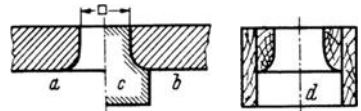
Abrundungen in Kernkästen. a = Werkzeichnung; b = Werkaufriß; c = Kern; d = Kernkasten.
